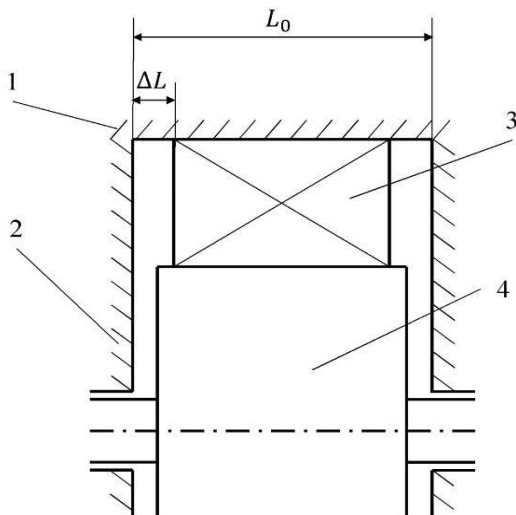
Поздовжній переріз пластинчато-роторного вакуумного насоса: 1 – статор; 2 – бокова кришка; 3 – лопатка; 4 – ротор
